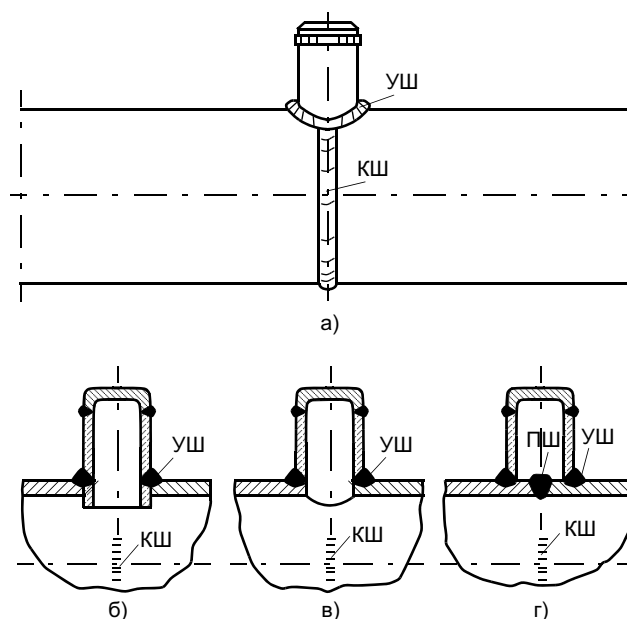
Ремонт ССС путем приварки штуцера-заклушки в зоне повреждения кольцевого шва (КШ): а — общий вид места приварки штуцера-заклушки угловым швом (УШ); б — соединение типа вварного штуцера, размещенного в отверстии; в, г — соединения типа приварного штуцера-заклушки на наружной поверхности труб соответственно в зоне отверстия (в) и зоне подварочного шва
